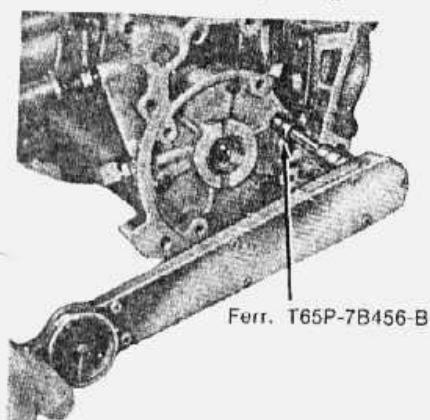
instalação dos parafusos da pista externa da embreagem uni-direcional
